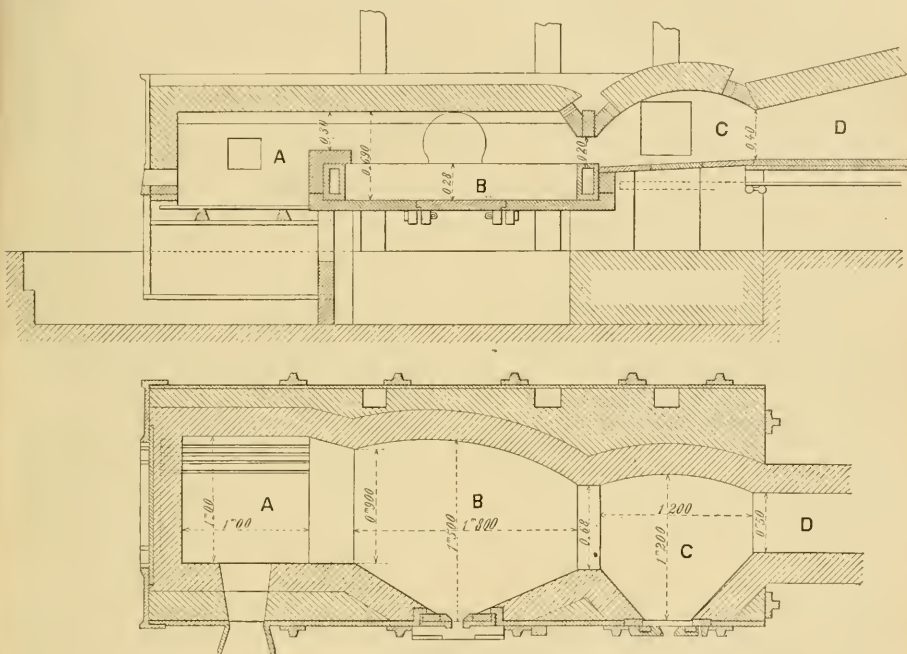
Four à puddler à cassin. — A, grille; B, sole de puddlage; C, cassin; D, rampant.
